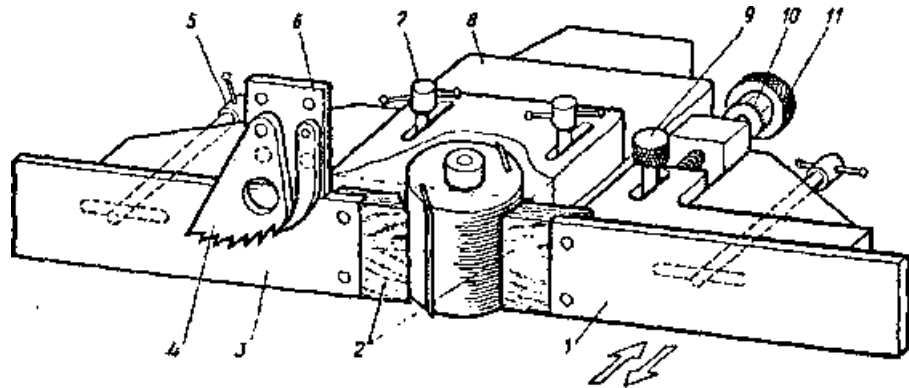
Налаштування направляючих лінійок фрезерного верстата:
